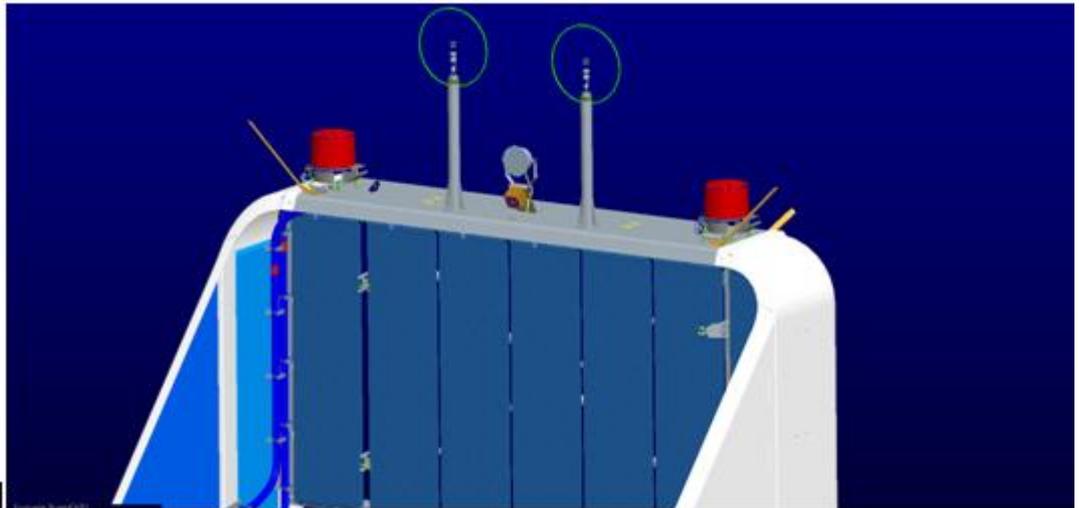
Ultraschall-Anemometer und Gefahrenfeuer an der Rückseite des Maschinenhausdaches (Mk-2-Variante des CoolerTop®)
